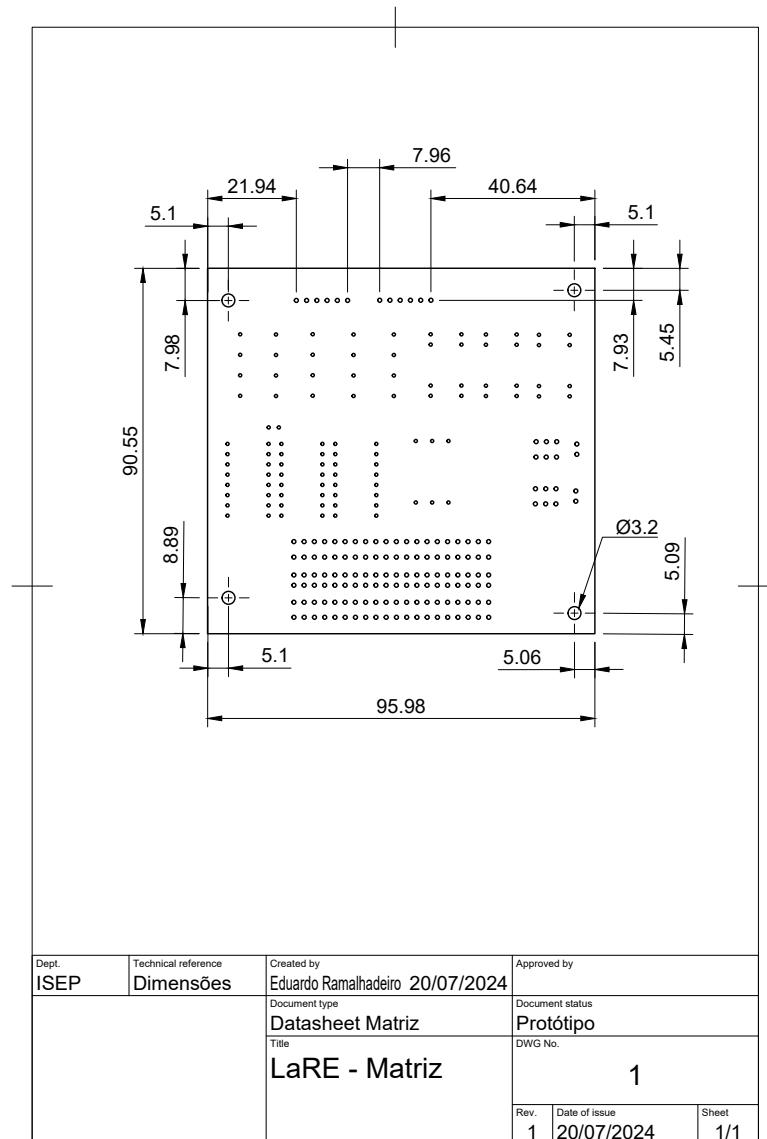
Dimensões mecânicas PC/104 - LaRE
